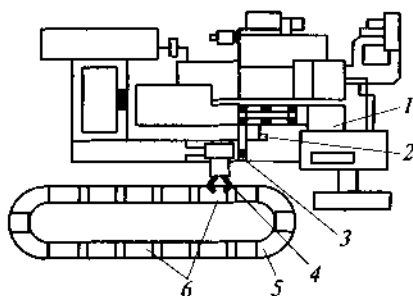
ГПМ на базе токарного станка с передним расположением робота:
